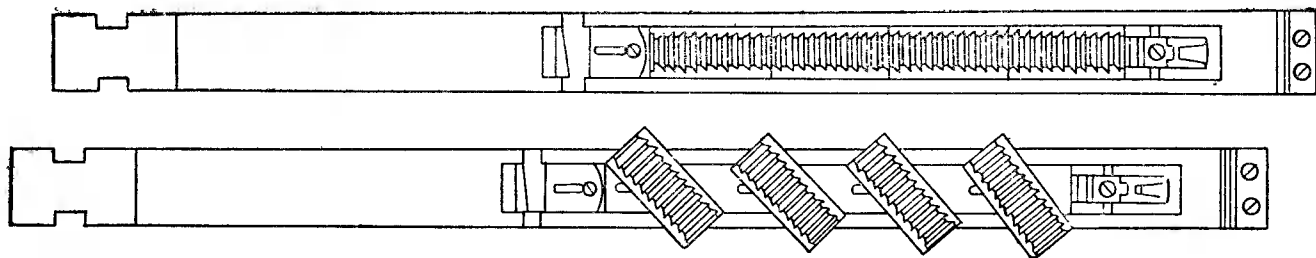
Наружная сборная протяжка с хвостовой частью для работы на горизонтально-протяжных станках общего назначения
